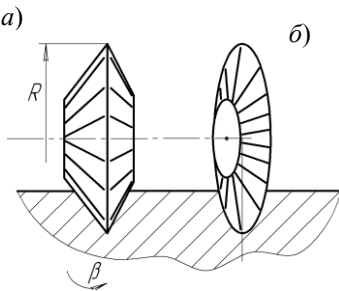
Формування профілю деталі лінією перетину конічних поверхонь
